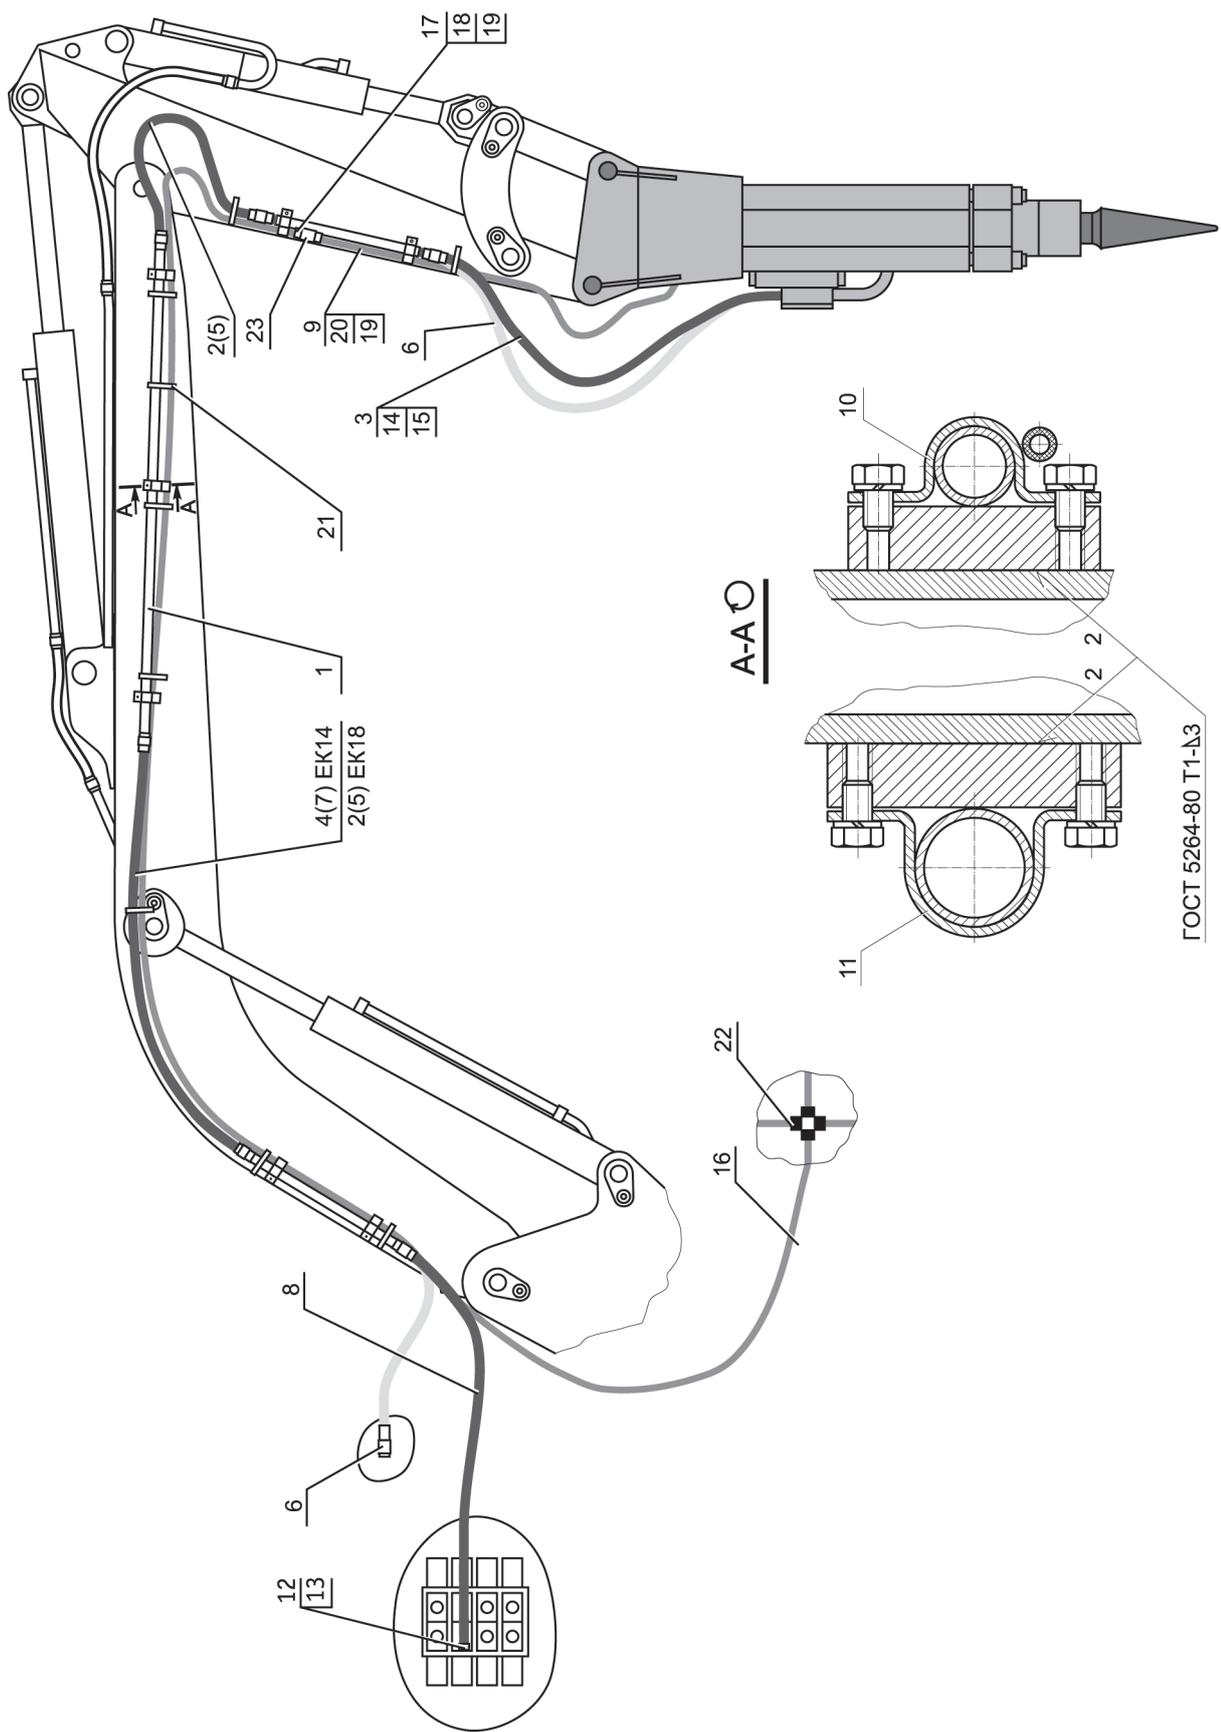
Монтаж гидрооборудования гидромолота на рабочем оборудовании экскаваторов EK-14, EK-18
